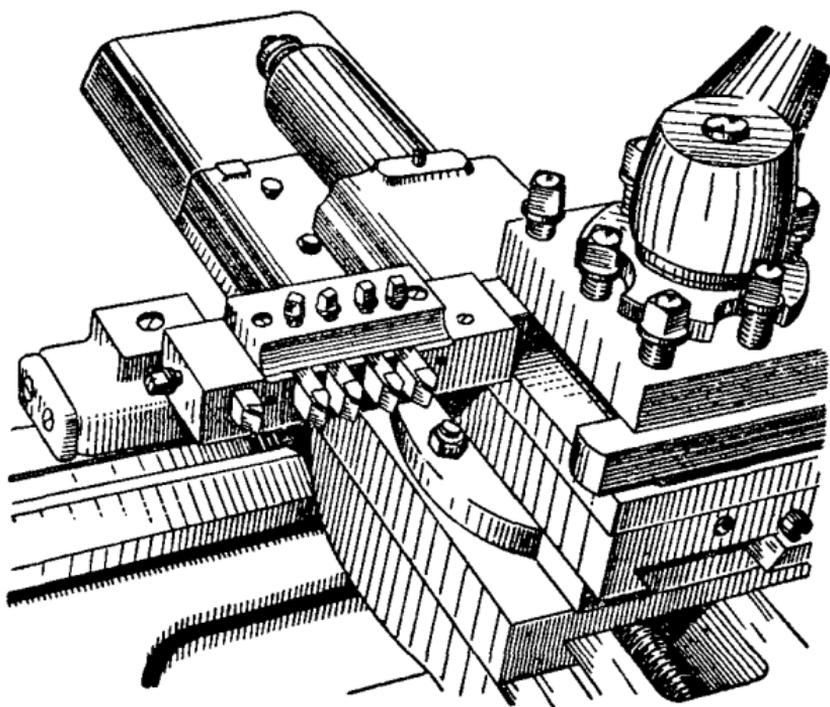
Приспособление для нарезания внутренней резьбы в гайках за один проход, установленное на токарном станке.
